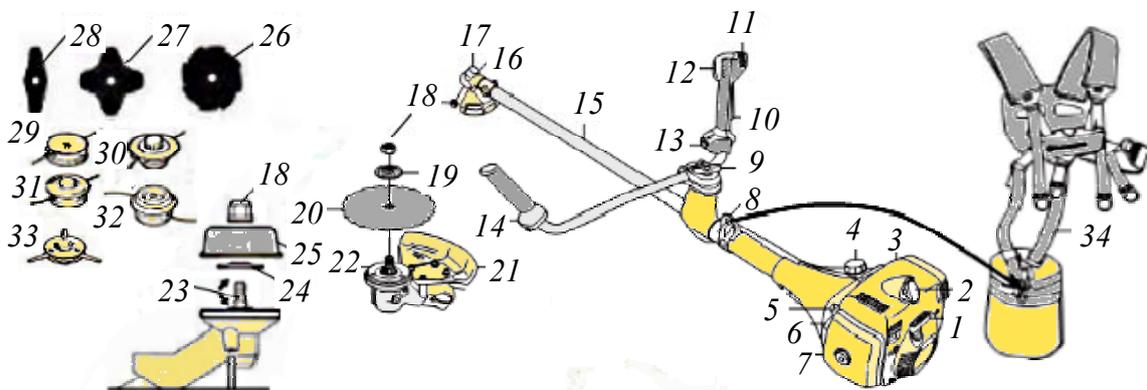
Мотокусторез Husqvarna 345FH: 1 – стартер; 2 – свеча зажигания; 3 – крышка; 4 – топливный бак; 5 – рычаг подсоса; 6 – топливный насос; 7 – крышка воздушного фильтра; 8 – подвеска ремней лямки; 9 – винт рукоятки; 10 – кнопка блокировки подачи топлива; 11 – выключатель двигателя; 12 – рычаг подачи топлива; 13 – подогрев рукояток; 14 – ручка левой руки; 15 – штанга; 16 – редуктор; 17 – пробка; 18 – гайка; 19 – шайба; 20 – зубчатый пильный диск; 21 – защита режущего органа; 22 – поводковый патрон; 23 – вал; 24 – нажимной диск; 25 – рабочая тарелка; 26 – восьмигранный диск; 27 – четырехгранный диск; 28 – нож; 29, 30 – двухнитевые головки ручной настройки; 31 и 32 – полуавтоматические двухнитевые головки; 33 – трехножевая пластмассовая косильная лопасть; 34 – лямка
